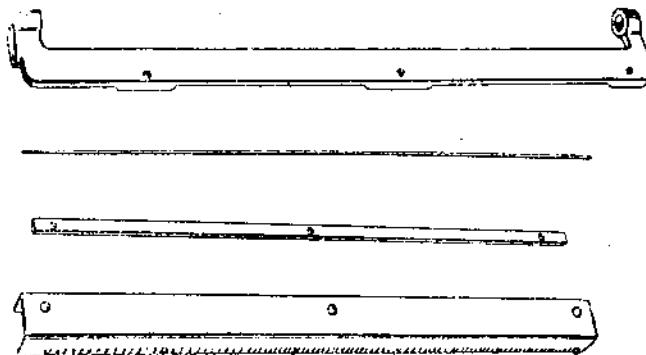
Направляющее и поддерживающее приспособление штанг.
